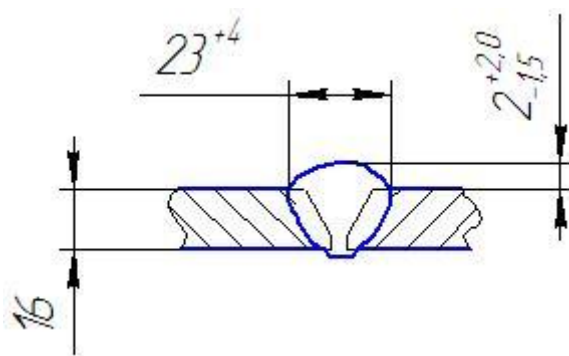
Размеры сварного шва при толщине трубопровода 16мм
